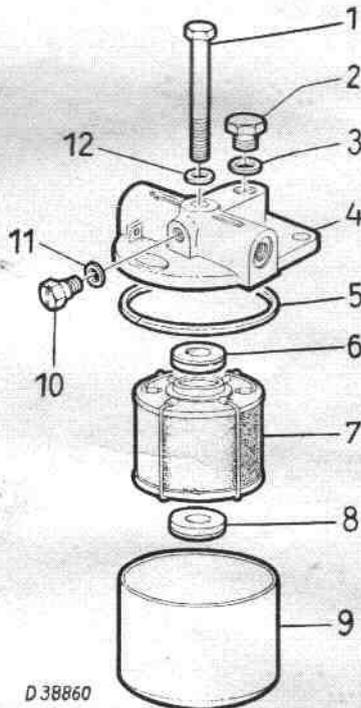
Filtre à combustible, ordre de remontage de l'ensemble
